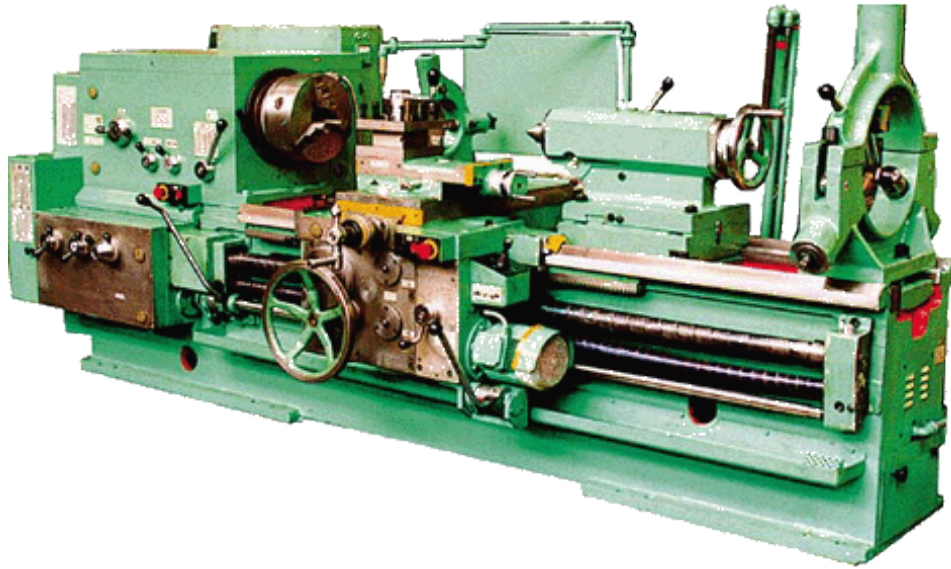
Токарно-гвинторізний верстат моделі 1М63
